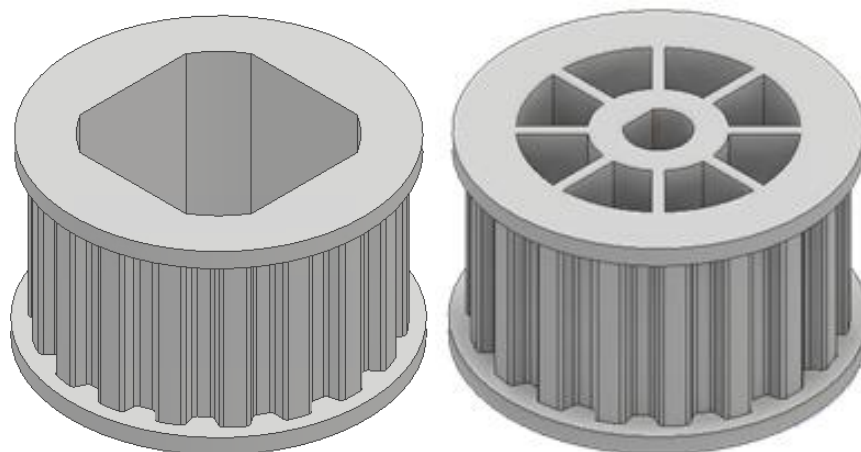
Зубчатое колесо для вала двигателя и держателя анода
